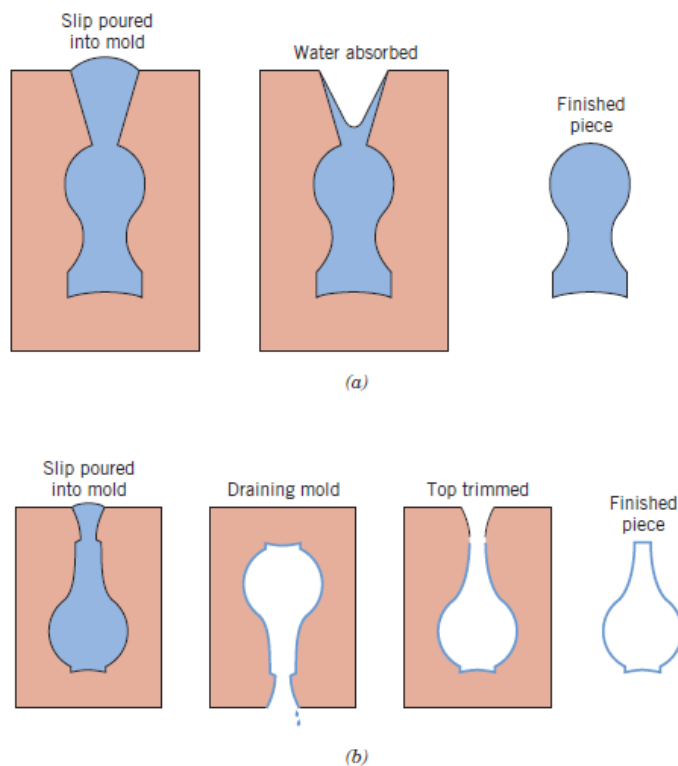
Secuencia de pasos para el solid-casting (a) y el slip-casting (b).
